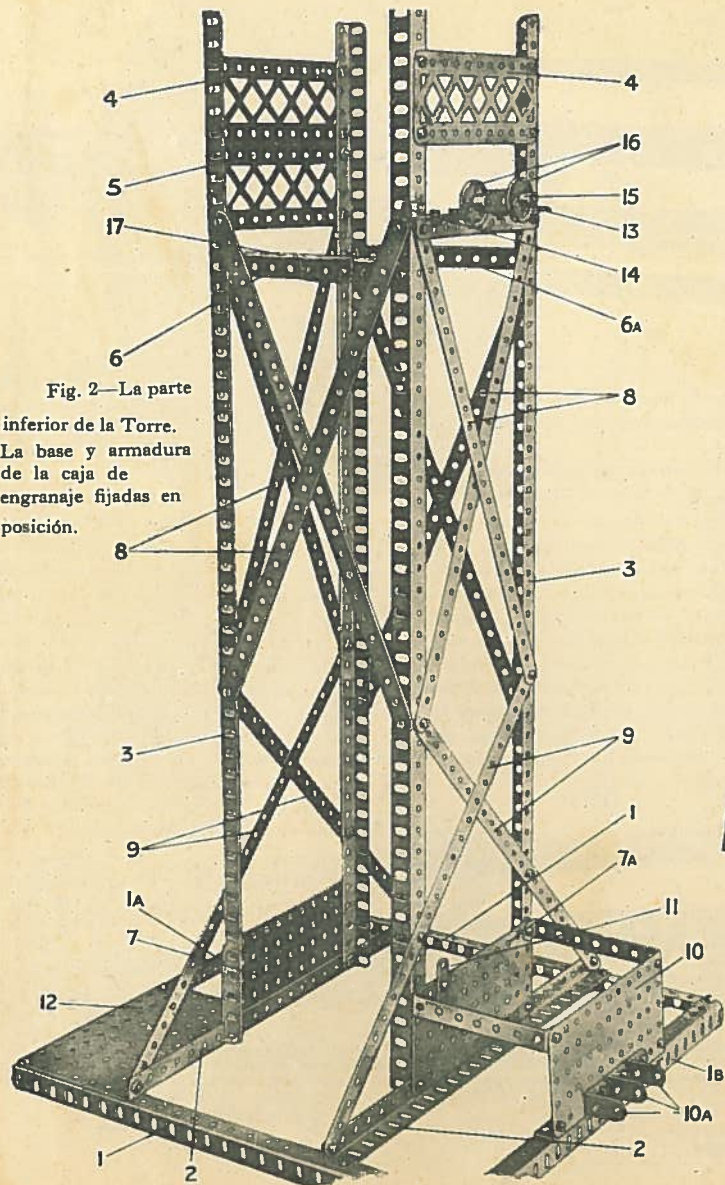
La parte inferior de la Torre. La base y armadura de la caja de engranaje fijadas en posición.
